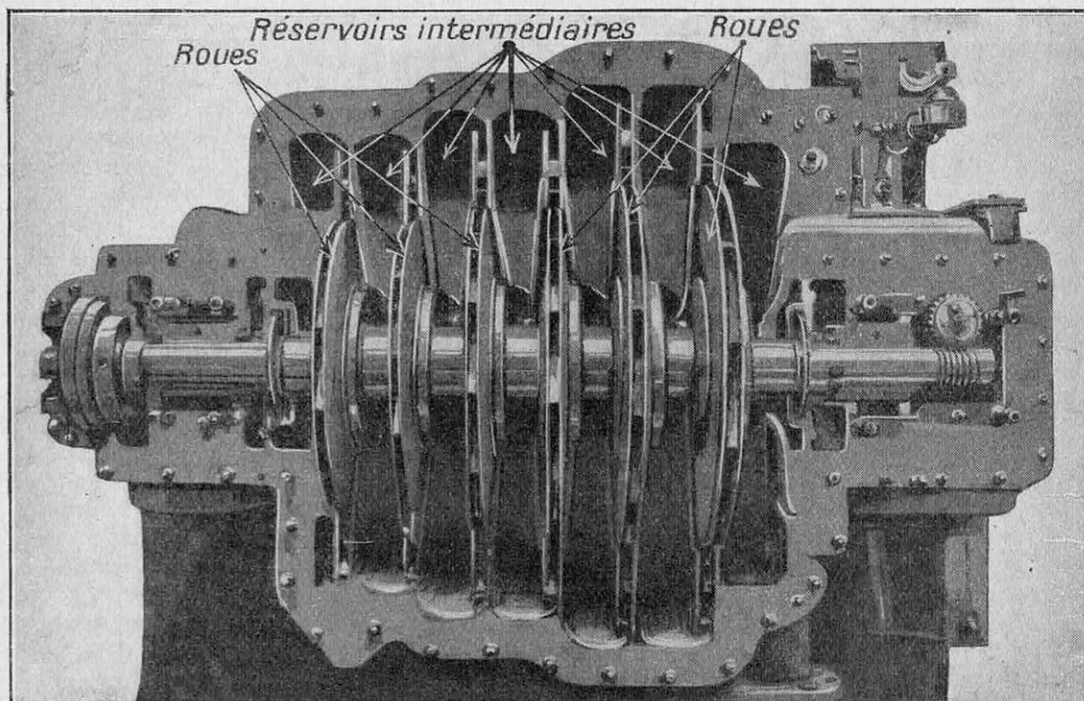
VUE INTÉRIEURE DU TURBO-COMPRESSEUR DE 600.000 FRIGORIES-HEURE
